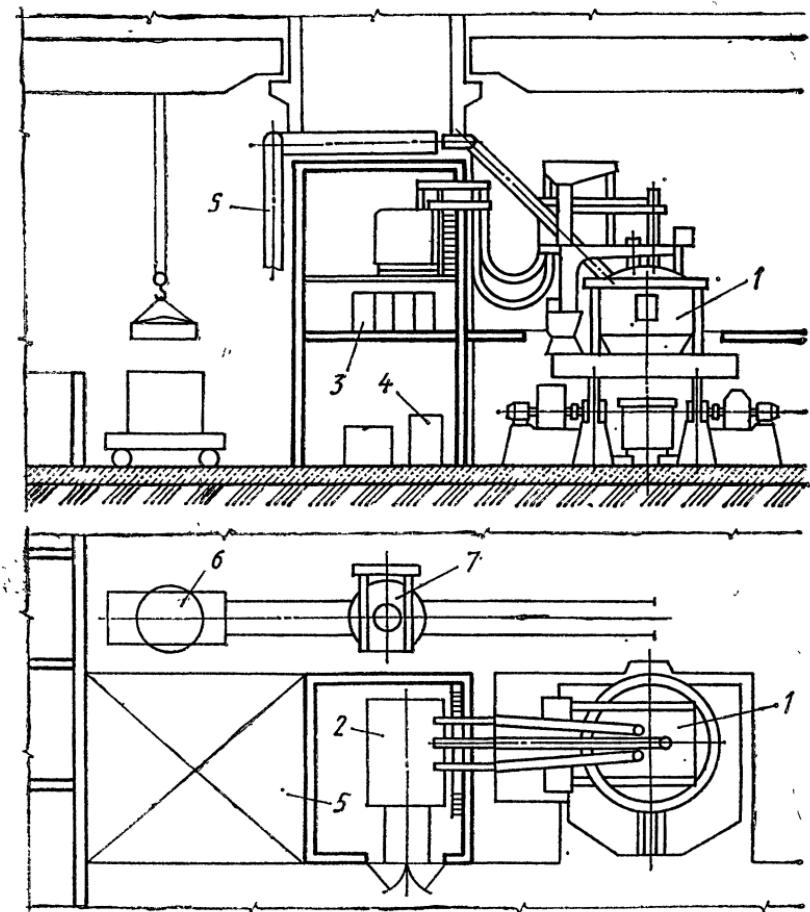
Дополнительное оборудование дуговой плавильной печи:
